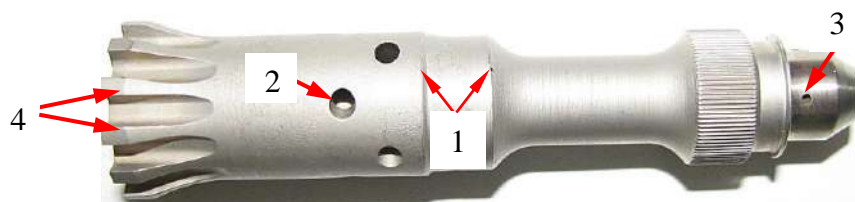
1 Внешний вид форсунки газогенератора. Стрелками показаны: 1 – местоположение сварного шва, 2 – отверстия окислителя, 3 – отверстие горючего, 4 - ребрение.
